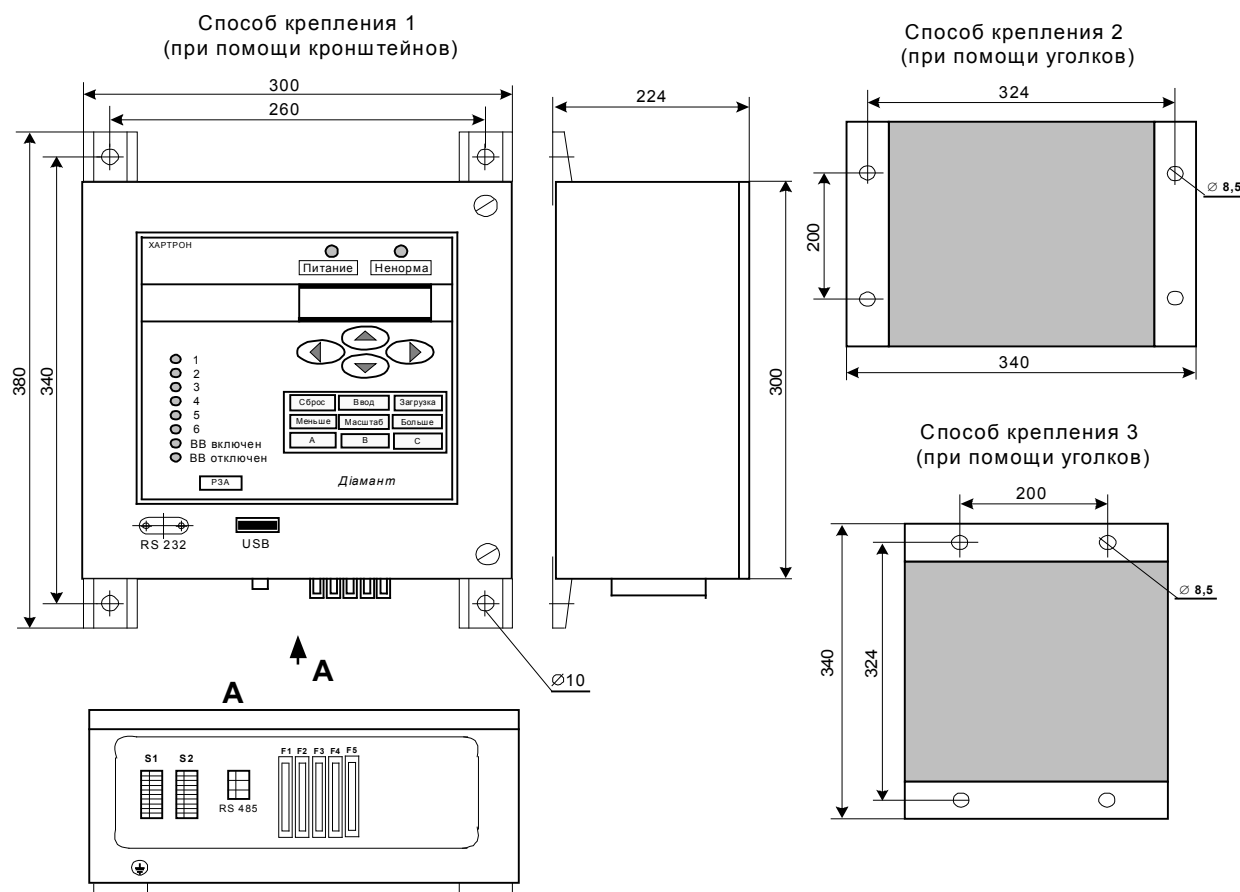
Габаритно – установочный чертеж ПМ РЗА
